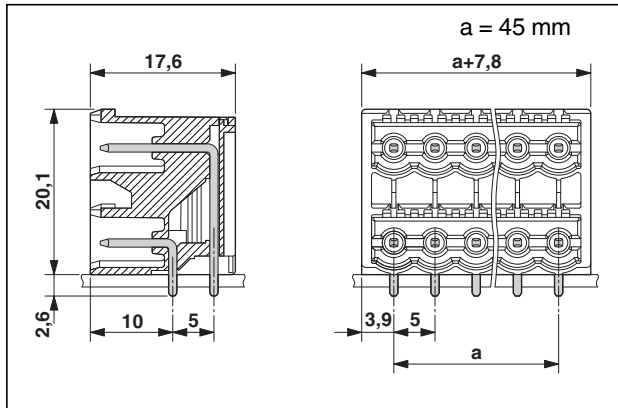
Abmessungen CCDN 2,5/10-G1 P26 THR
